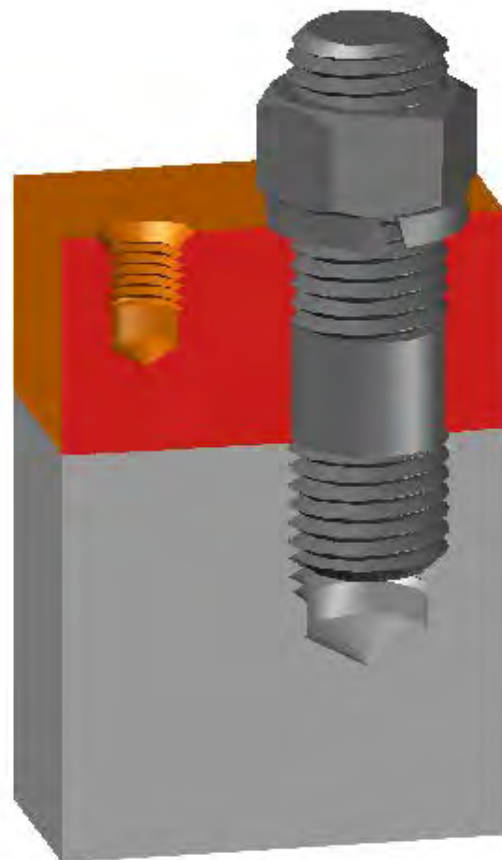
Модели сборки деталей шпилькой цельная и в разрезе
